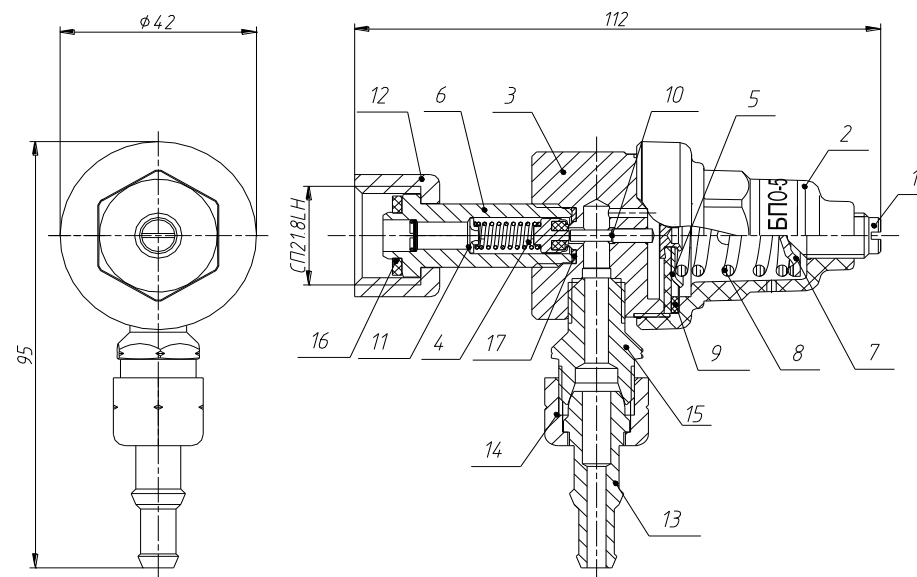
Редуктор баллонный пропановый одноступенчатый:
